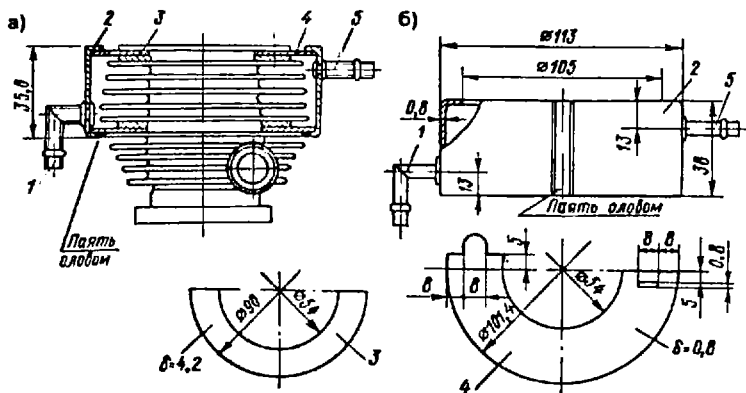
Конструкция рубашки охлаждения двигателя: а — установка рубашки на цилиндр двигателя; б — конструкция рубашки.
